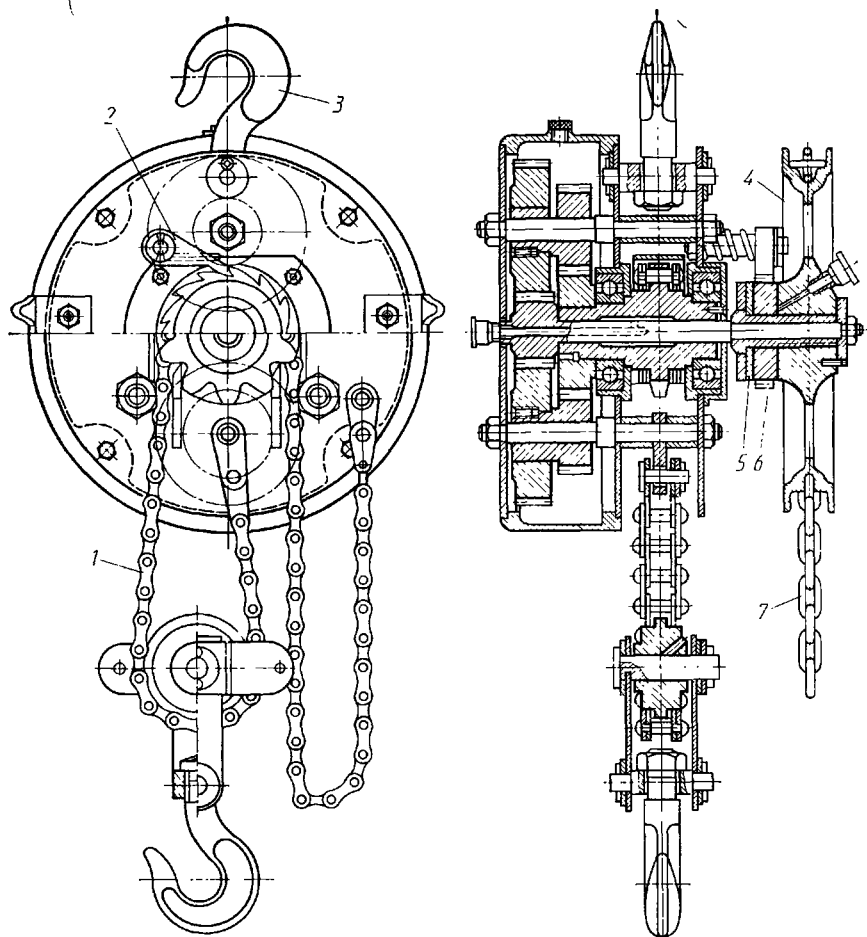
Таль с ручным приводом с соосной зубчатой передачей
